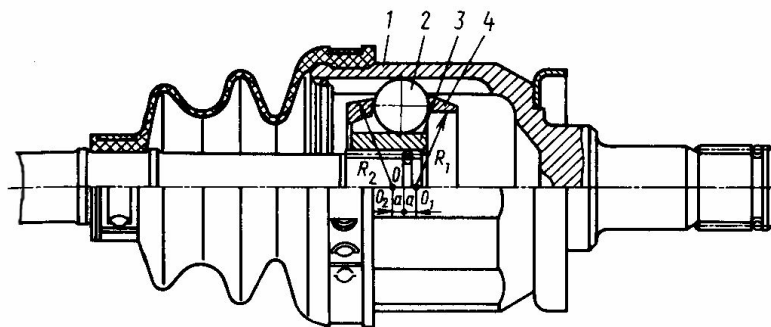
Универсальный шестишариковый карданный шарнир (типа ГКН)
